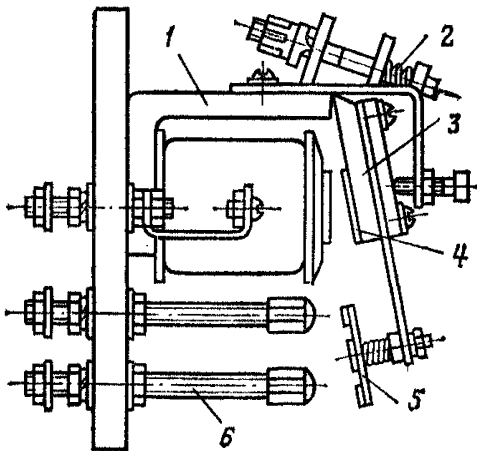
Реле типов РЭ-100 и РЭ-180: 1 — сердечник; 2 — возвращающая пружина; 3 — якорь; 4 — немагнитная прокладка; 5 — контактный мостик; 6 — стойка неподвижного контакта
